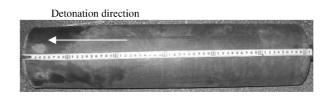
爆炸复合后形貌 Fig. 3 Pattern after explosive clad
